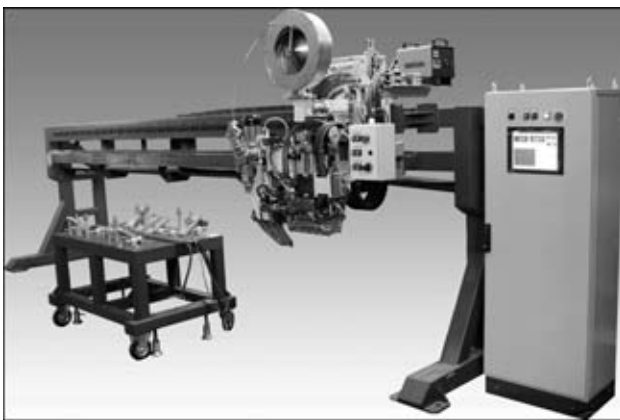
Установка портального типа для сварки в узкий зазор соединений титана и сплавов на его основе толщиной 20...110 мм
